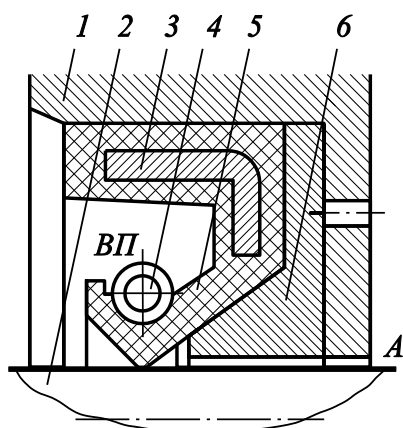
Конструктивная схема стандартной манжеты с опорным конусом: 1 – корпус гидроустройства; 2 – вал; 3 – каркас; 4 – пружина; 5 – корпус манжеты; 6 – опорный конус
